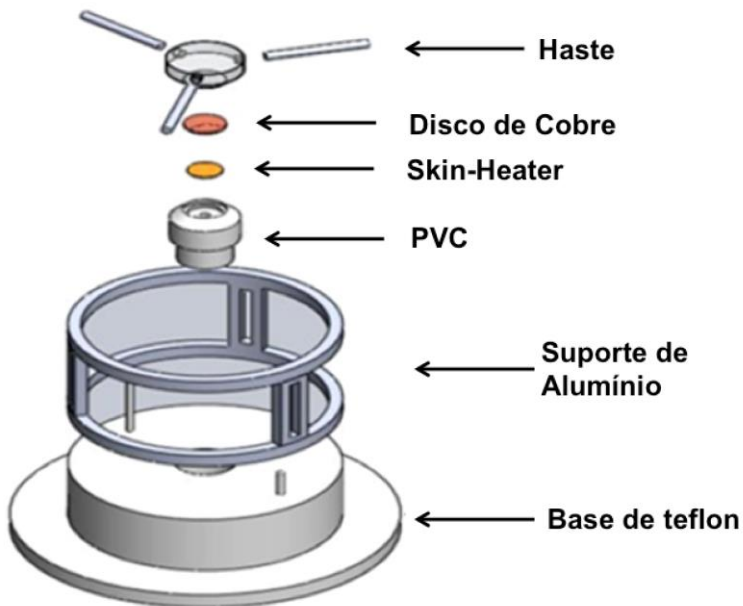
Vista explodida da seção de teste e elemento confinador.
